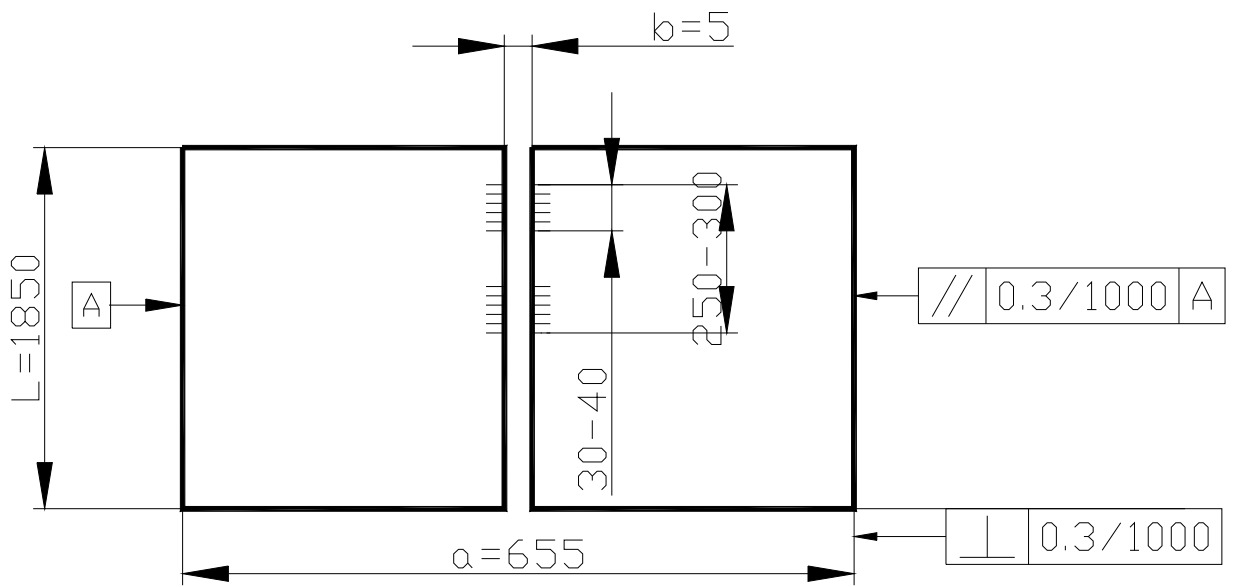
Эскиз к операции 08. Сборка заготовки под сварку
